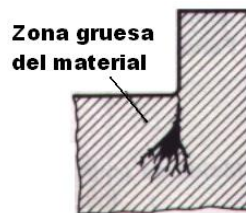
Grietas en la estructura de la fundición
